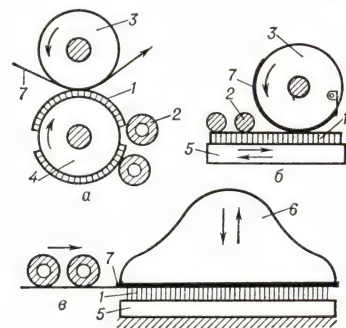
Схемы построения печатных аппаратов: а — ротационный; б — плоскочислительный; в — тигельный; 1 — печатная форма; 2 — накатные валики красочного аппарата; 3 — печатный цилиндр; 4 — формный цилиндр; 5 — талер; 6 — тигель; 7 — бумага.
